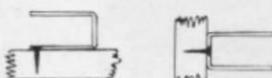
Das Relais sollte möglichst in waagrechter Lage befestigt werden. Normalerweise wird die Schutzhäube einfach mit zwei Holzschrauben auf oder unter dem Grundbrett befestigt (links). Bei hängender Montage (rechts) erfolgt die Befestigung sinngemäß durch seitliches Durchbohren und Anschrauben.
